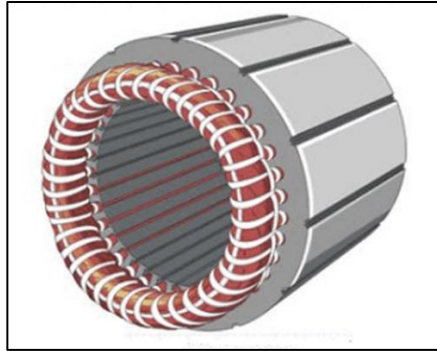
COMPONENTE DEL MOTOR – ESTATOR
